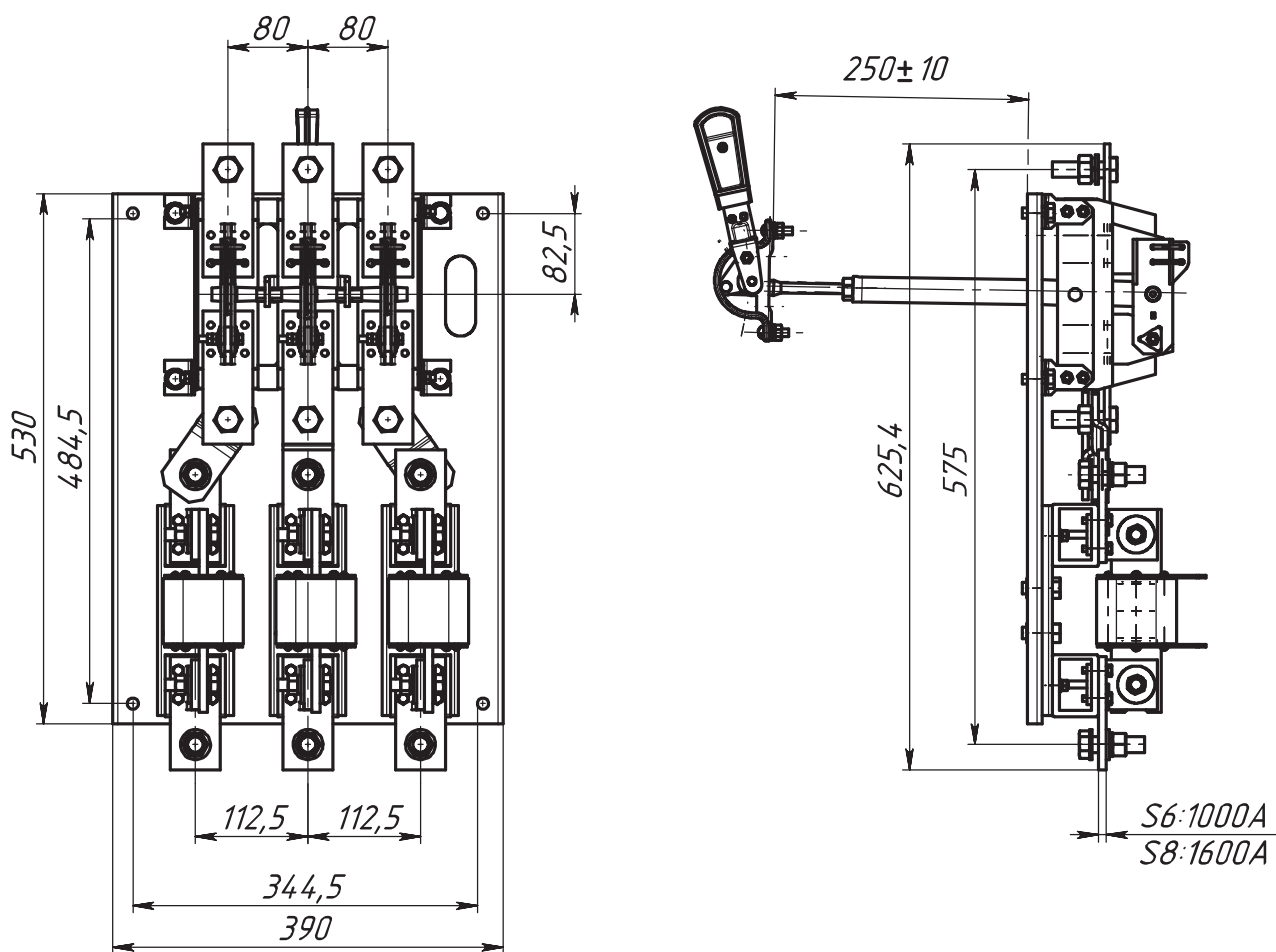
Разъединители-предохранители с центральным приводом на токи 1000 А и 1600 А
